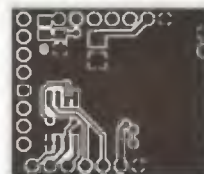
Univerzální deska s plošnými spoji modulu - strana Bottom
